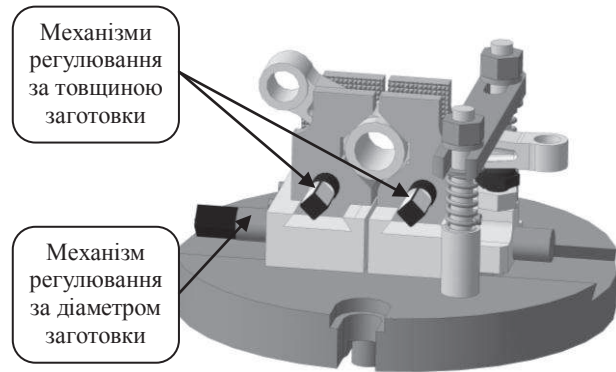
Переналаджуваний установлювально-затискний модуль для обробки деталей типу важелів
